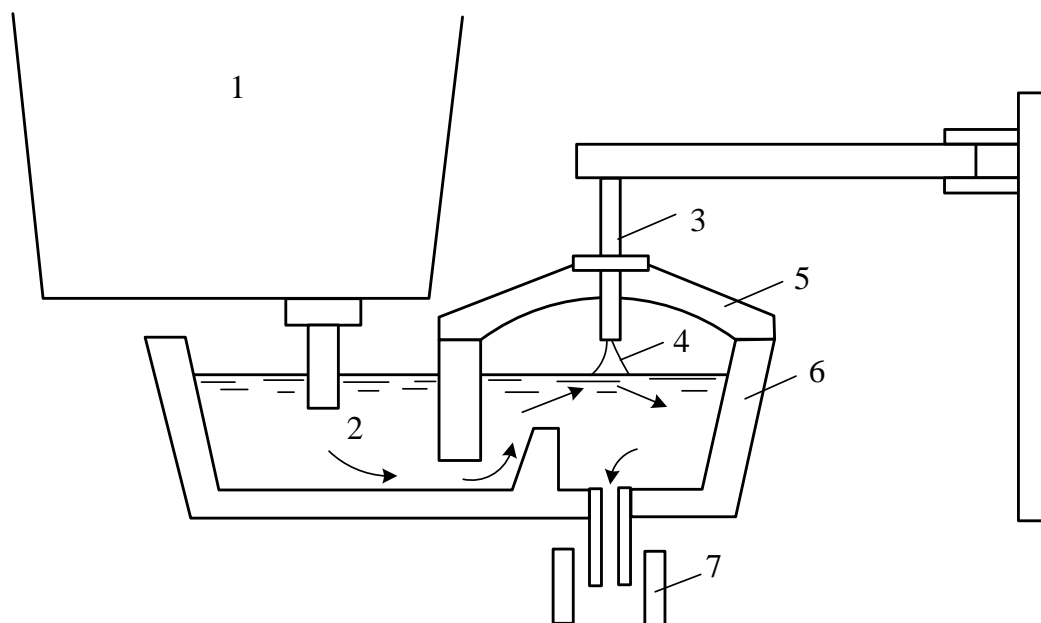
Общий вид установки плазменного нагрева на промежуточном ковше: 1 – разливочный ковш; 2 – поток жидкой стали; 3 – плазмотрон; 4 – плазменная дуга; 5 – огнеупорная крышка; 6 – камера нагрева; 7 – кристаллизатор
